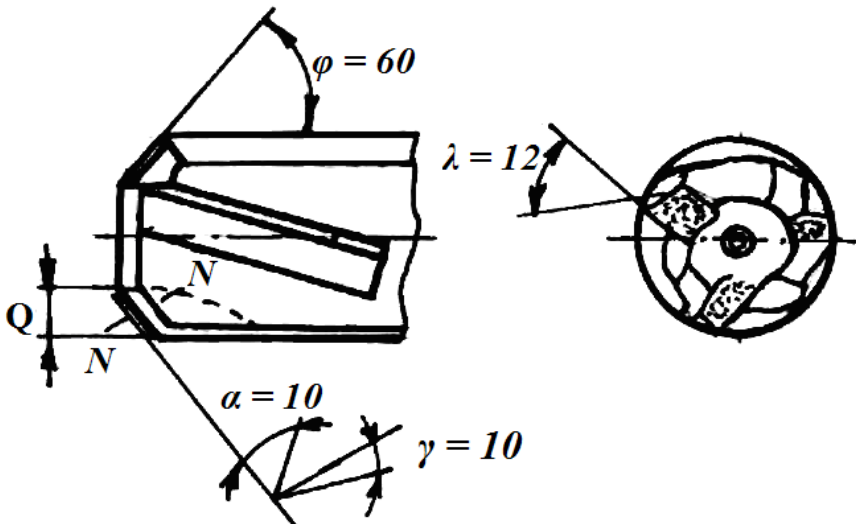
Трьохзубий зенкер з впаяними пластинками твердого сплаву
